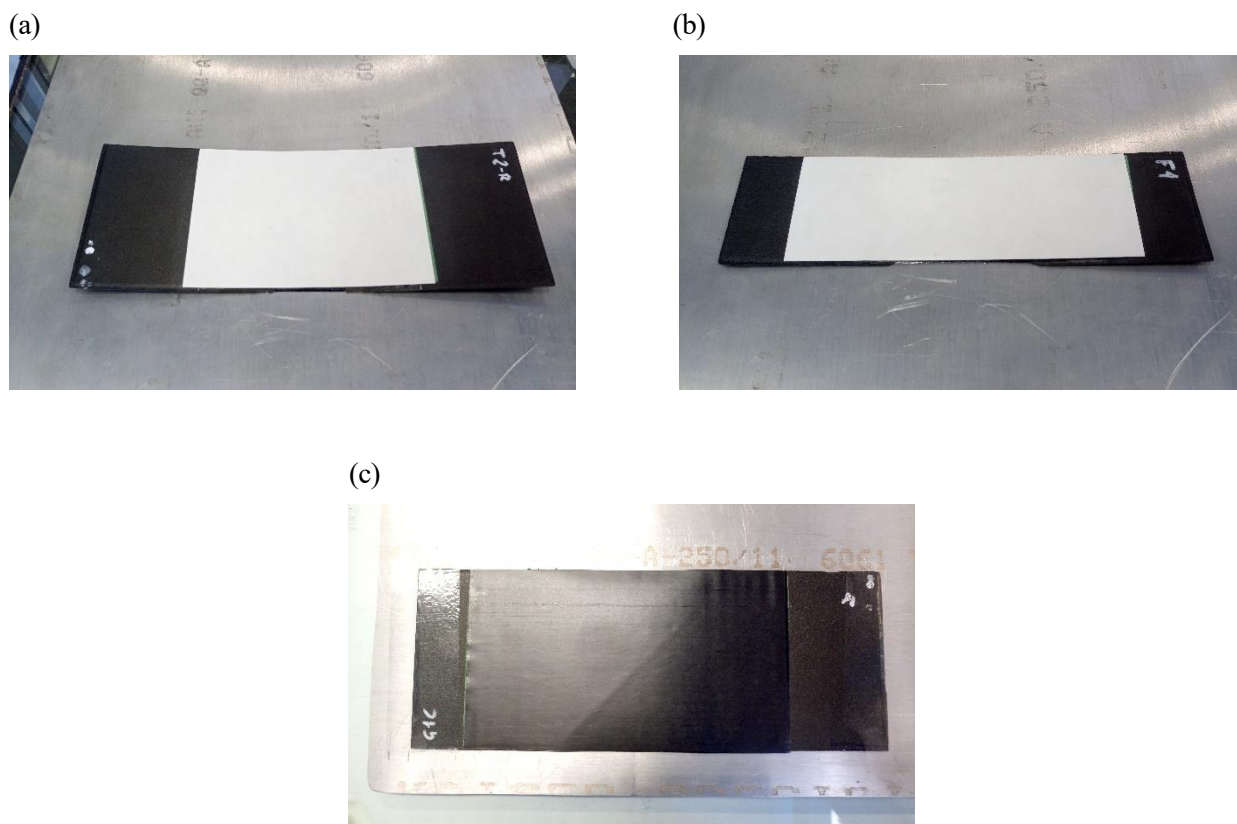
(a) Parche apilado en el panel tipo 3, (b) Parche apilado en el panel tipo 2 y, (c) Parche apilado en el panel tipo 1
